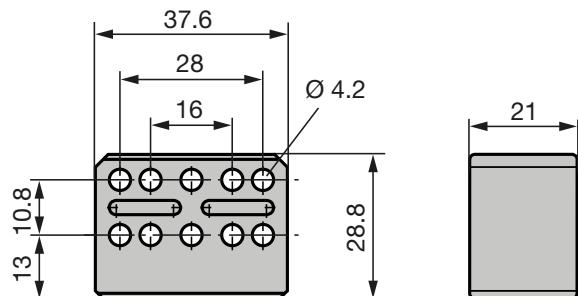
Dimensioni di ingombro datore di posizione BTL6-A-3800-2
